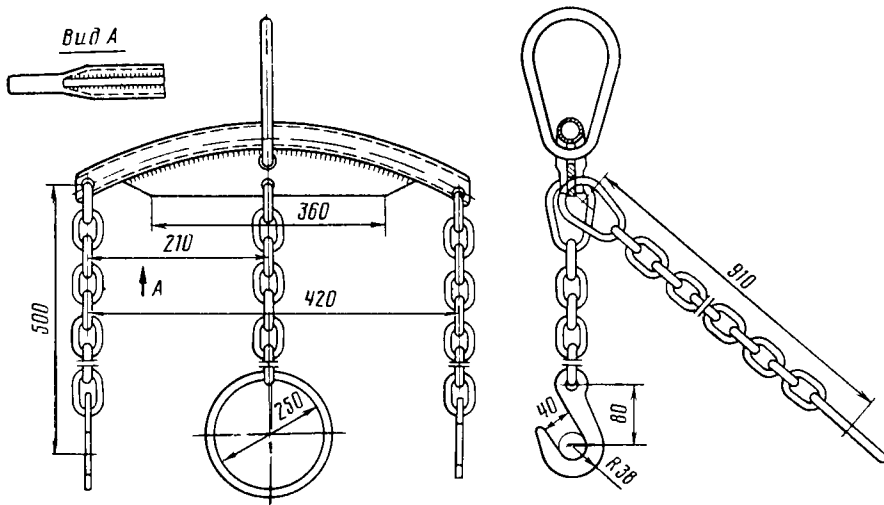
Приспособление для подвески силового агрегата и двигателя к подъемному устройству
